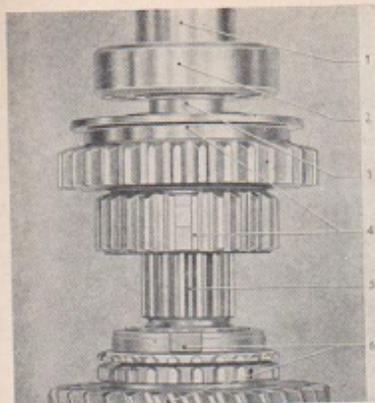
Synchrokörper für 1. Gang mit Schiebemuffe, Halblech und Kugellager auf Hauptwelle aufpressen
